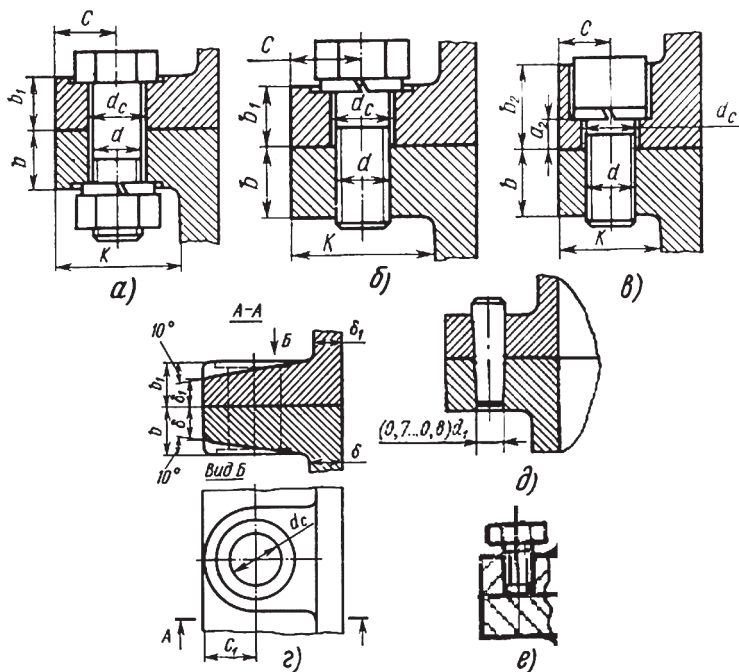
Способы крепления крышки к корпусу редуктора
